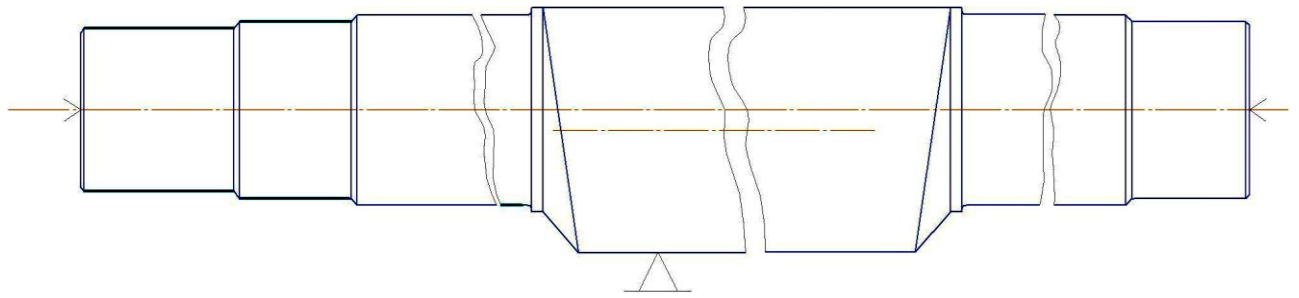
Ескіз схему базування деталі при виконанні контролю
